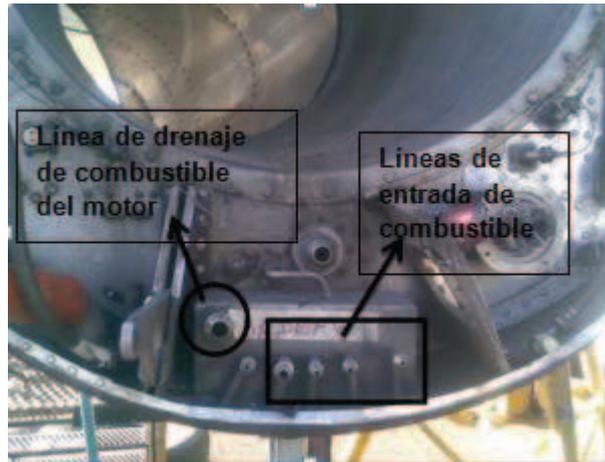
Líneas de entrada y drenaje de combustible del motor.
